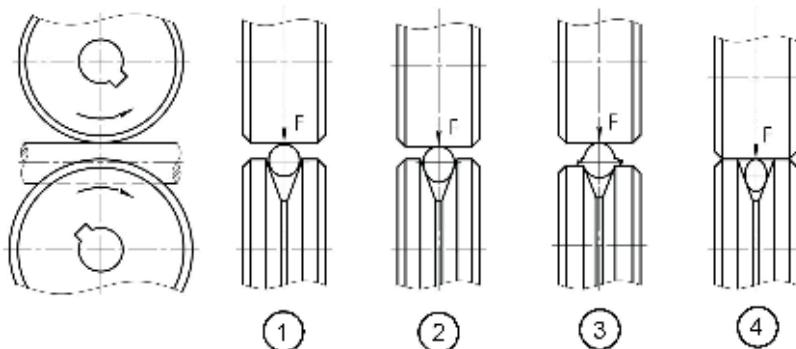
Усилие зажатия сварочной проволоки.
